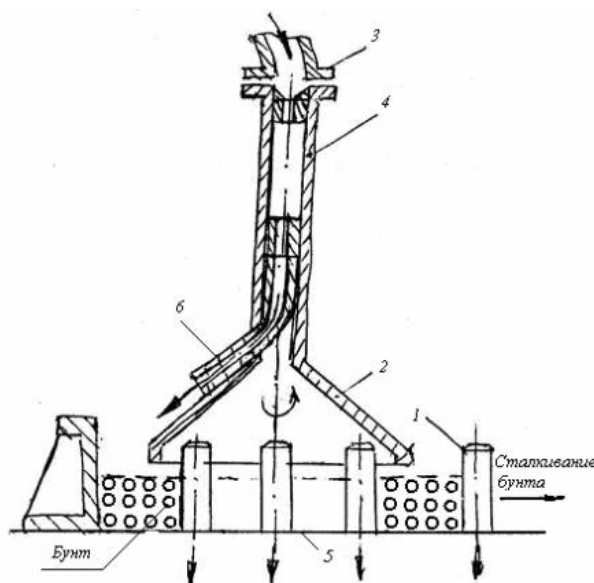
Дротова моталка з нерухомим бунтом: 1 – пальці; 2 – конус; 3 – приймальна трубка; 4 – порожнистий вал; 5 – плита; 6 – проводка
